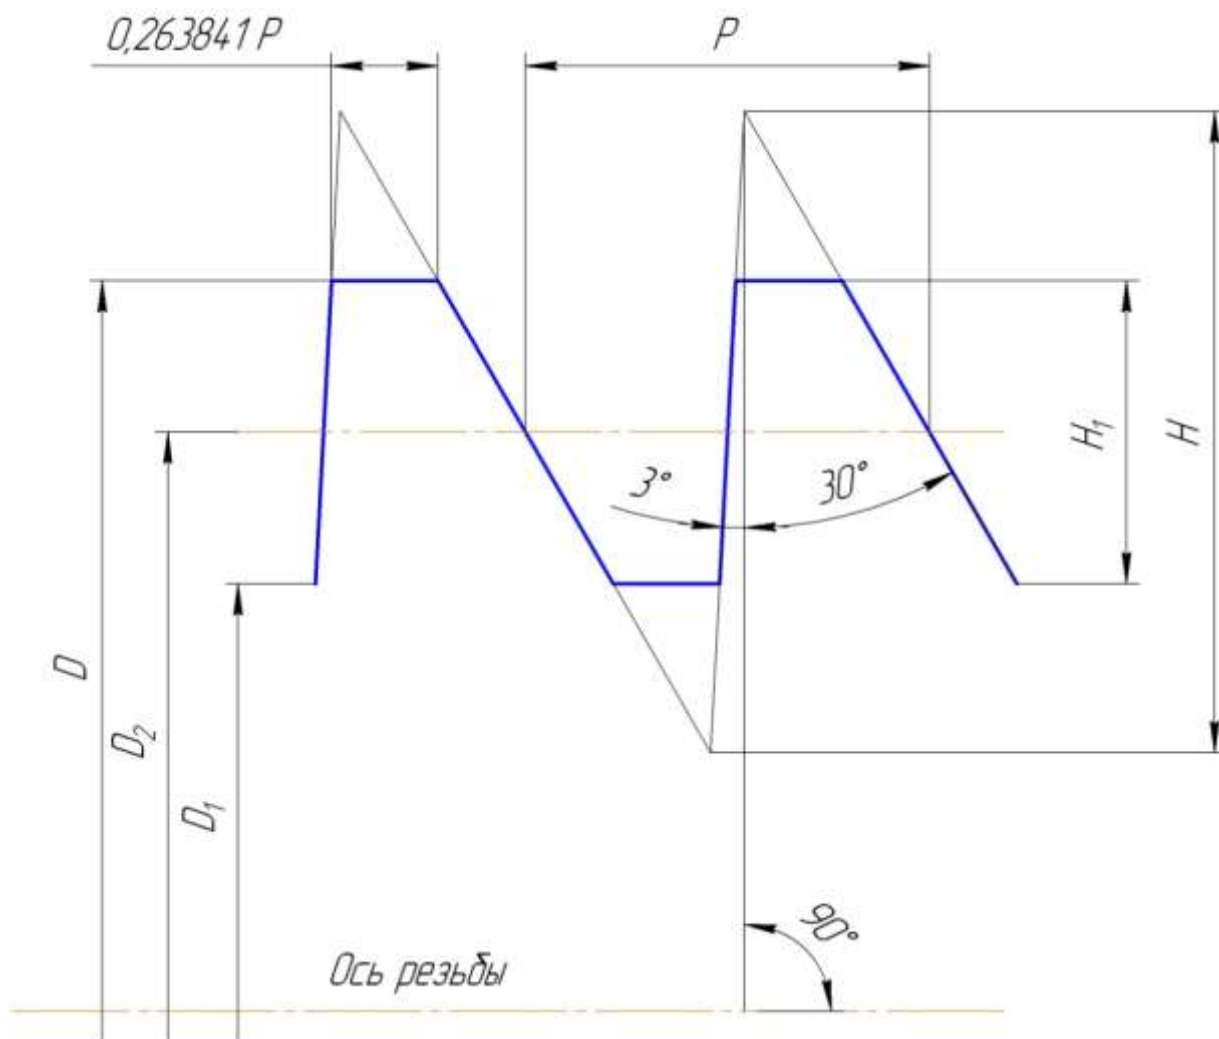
Номинальный профиль резьбы и его размеры
